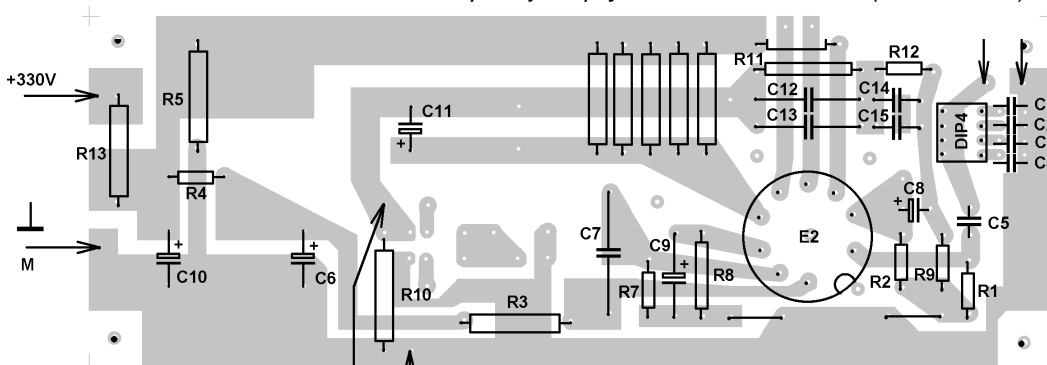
Deska s plošnými spoji linkových zesilovačů (86 x 180 mm)
